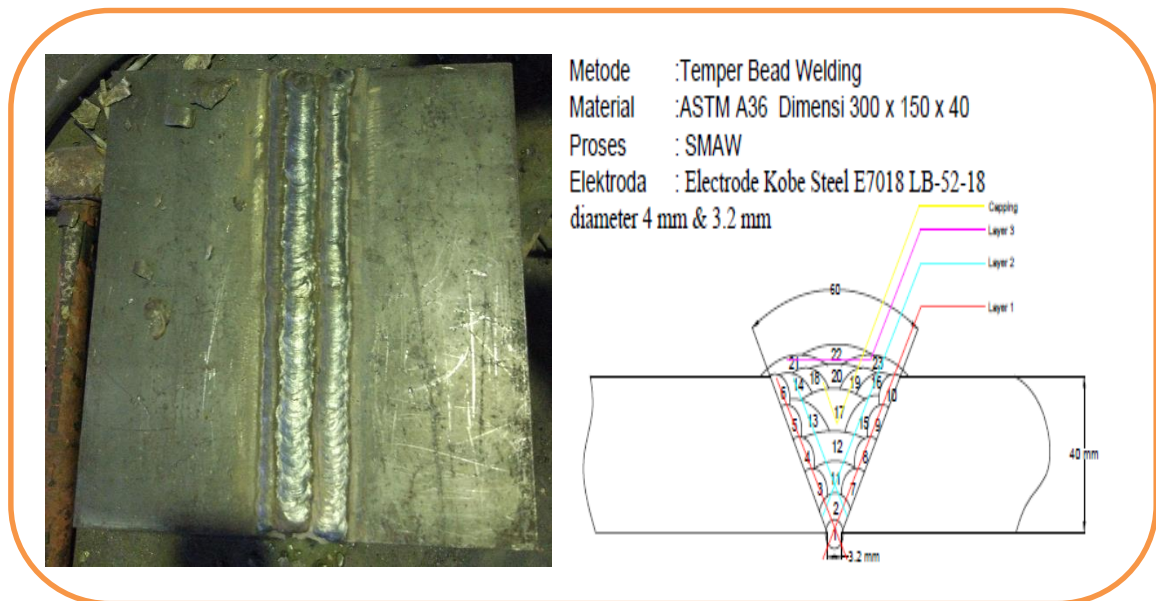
Demo Heat input Temper Bead Welding
